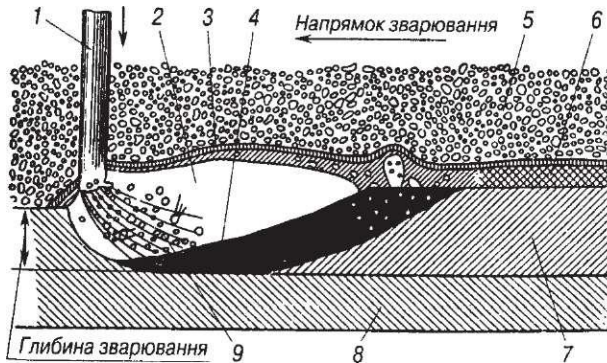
Схема горіння зварної дуги під флюсом:
